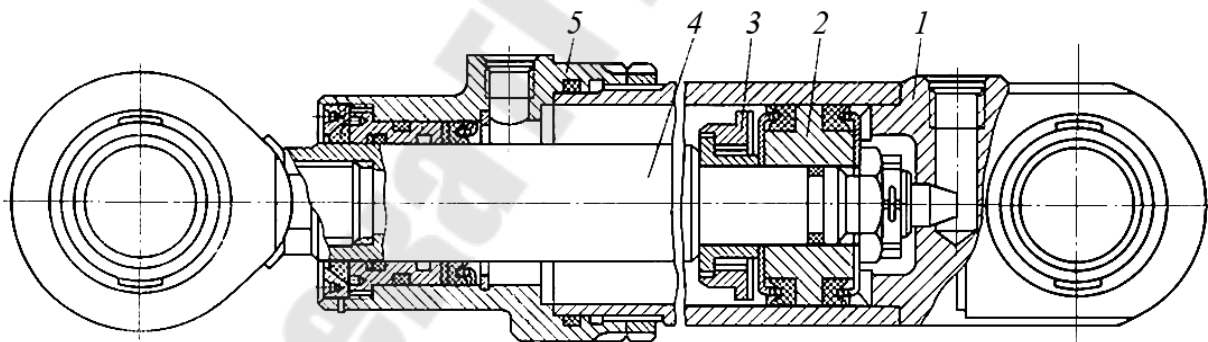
1. Конструкция поршневого цилиндра с двумя рабочими полостями
